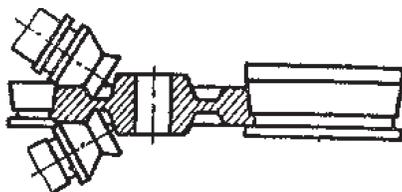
Раскатка обода и прокатка железнодорожных колес
